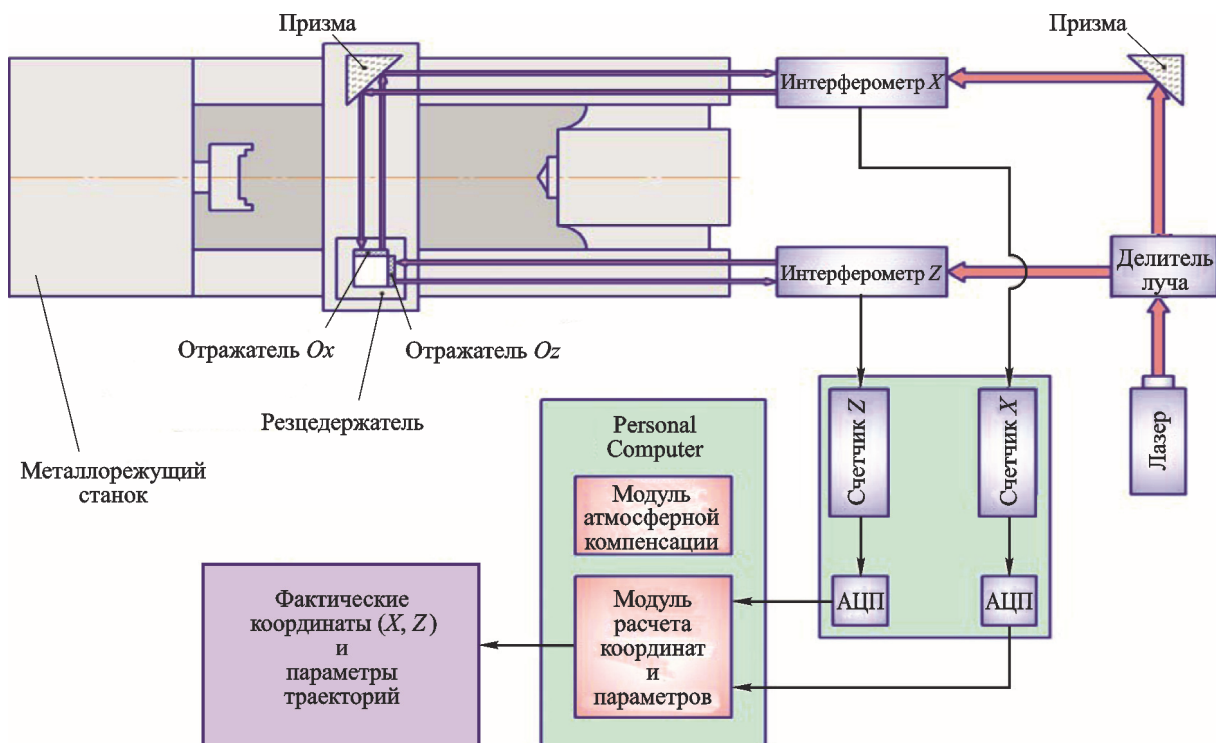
Блок-схема определения фактических координат формообразующей точки движущегося суппорта токарного станка
